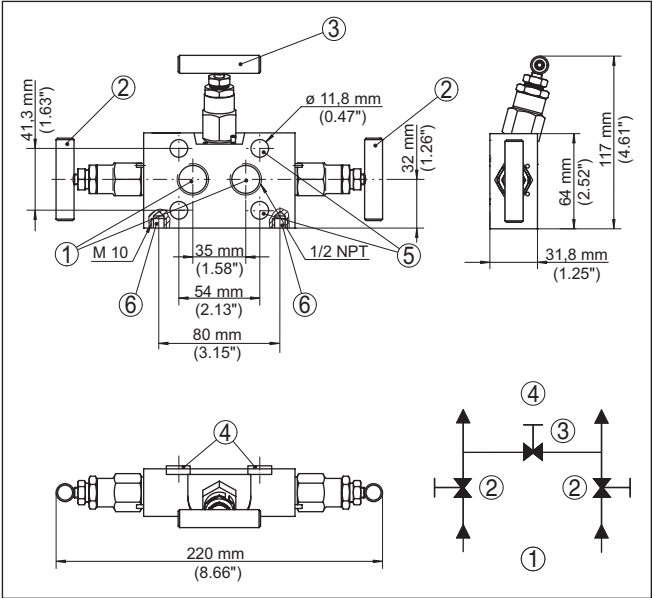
Construção bloco de 3 válvulas conforme EN 61518
